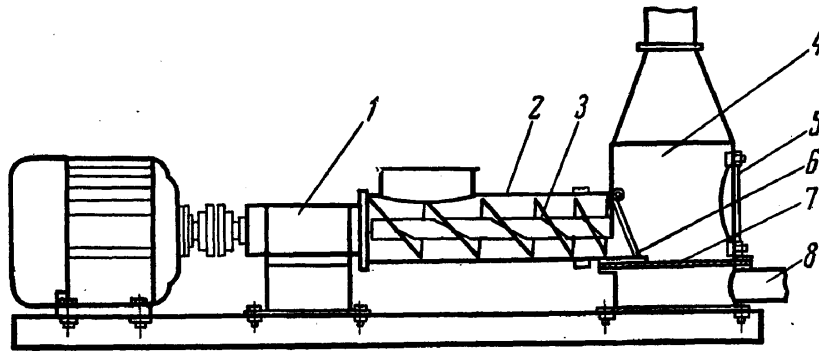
Шнековий живильник: 1 – корпус підшипника; 2 - корпус шнекової камери; 3 – шнек; 4 – аераційна камера; 5 – кришка; 6 – клапан; 7 – бельтингова перегородка; 8 – патрубок для стисненого повітря.
